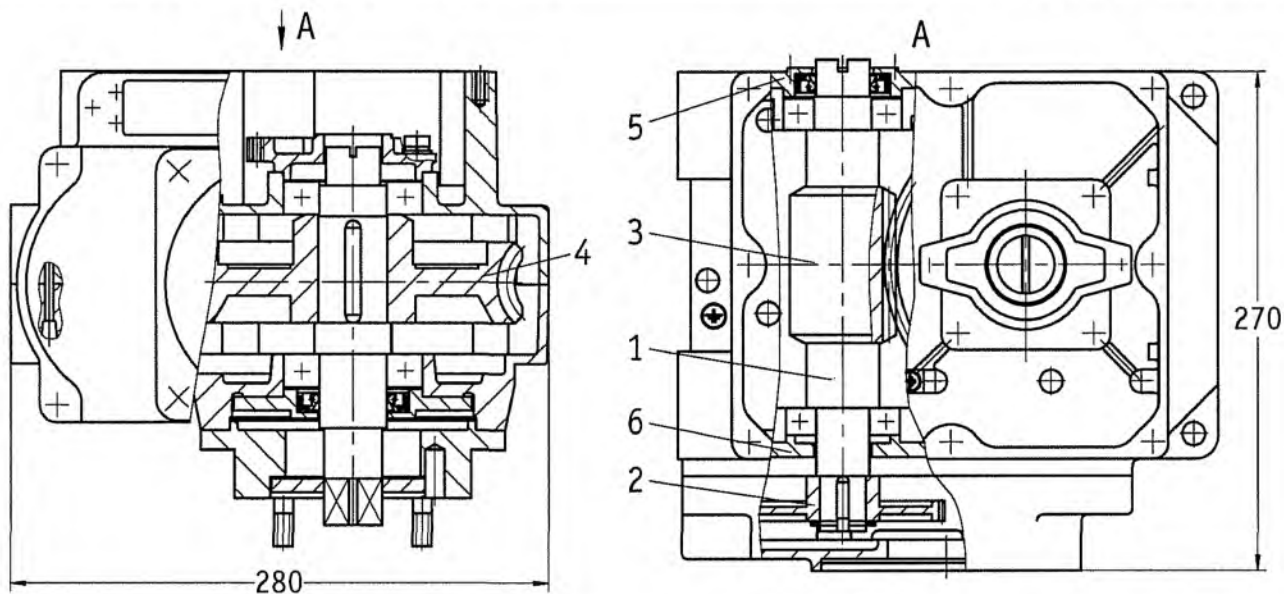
Редуктор фланцевого исполнения механизмов «МЭ0-16»
